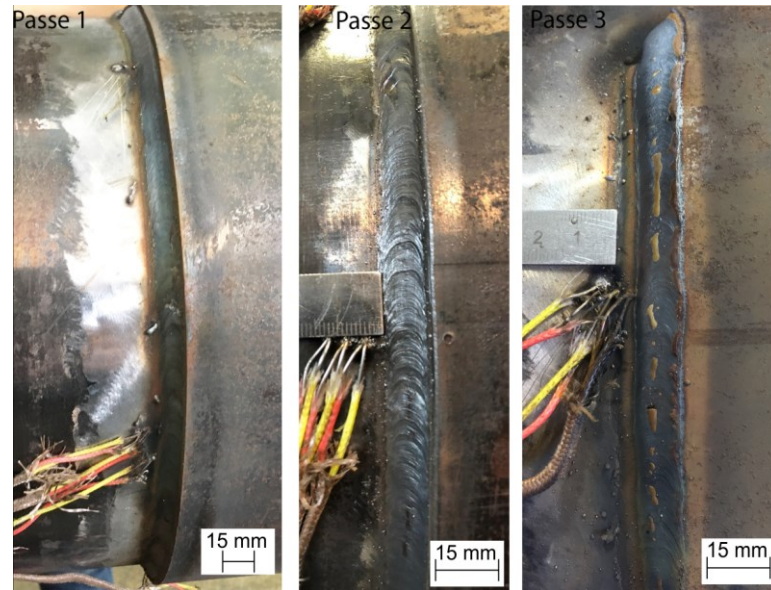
Soldagem orbital mecanizada de dupla calha tipo-B com GMAW-P AC sem pré-aquecimento.
